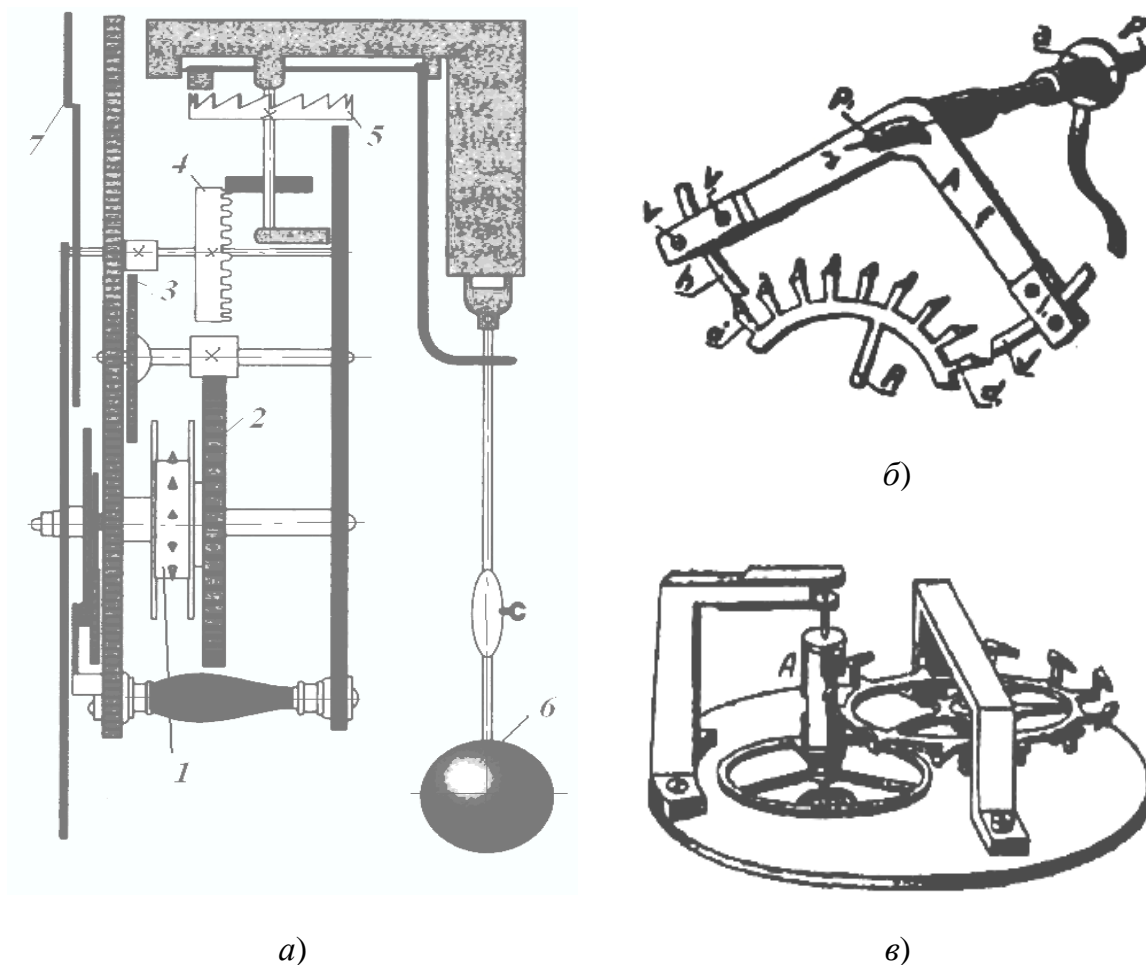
Схема механизма маятниковых часов (по рисунку Х. Гюйгенса): *а* – со шпindelным спуском: 1 – звездочка; 2, 3 – зубчатые передачи; 4 – коническая передача; 5 – анкерный спуск; 6 – маятник; 7 – циферблат; *б* – якорно-анкерный спуск; *в* – цилиндрический спуск
